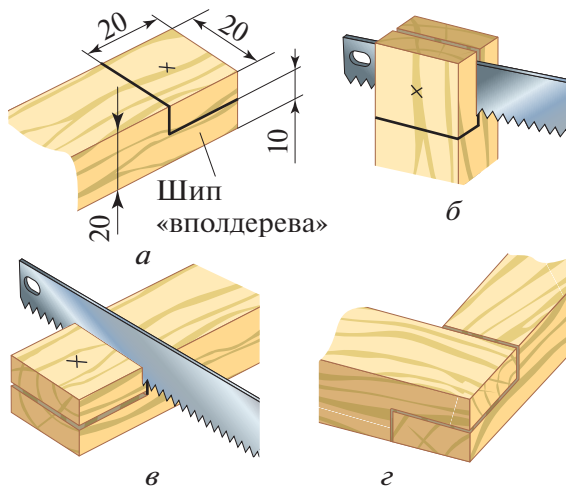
Последовательность изготовления шипа «вполдерева»:
